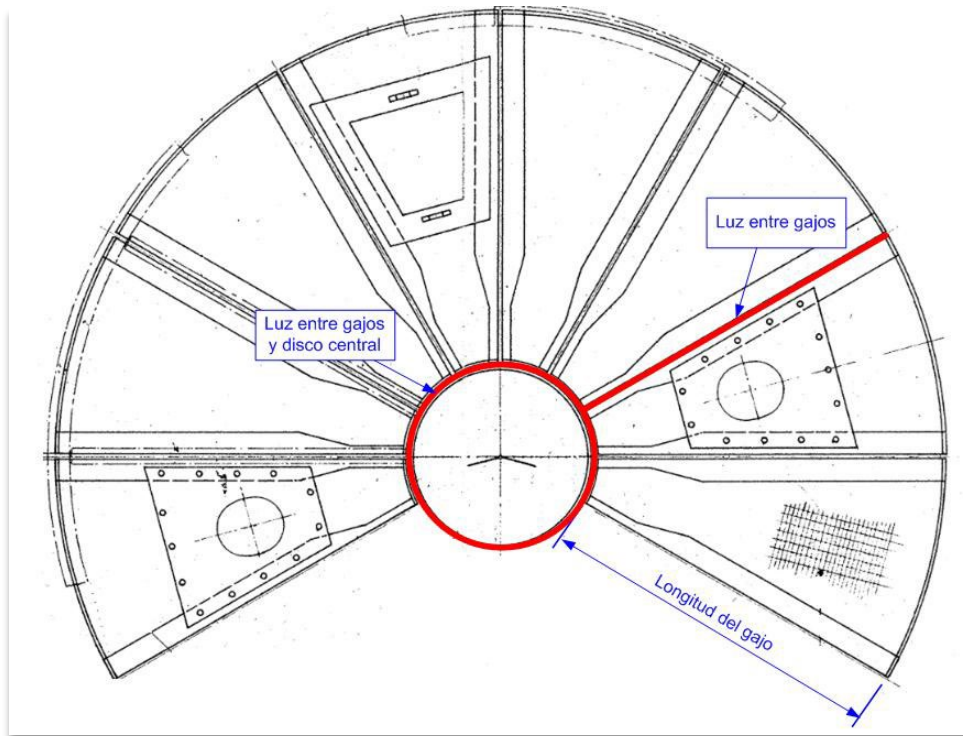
Detalle de montaje de piezas de la grilla soporte
